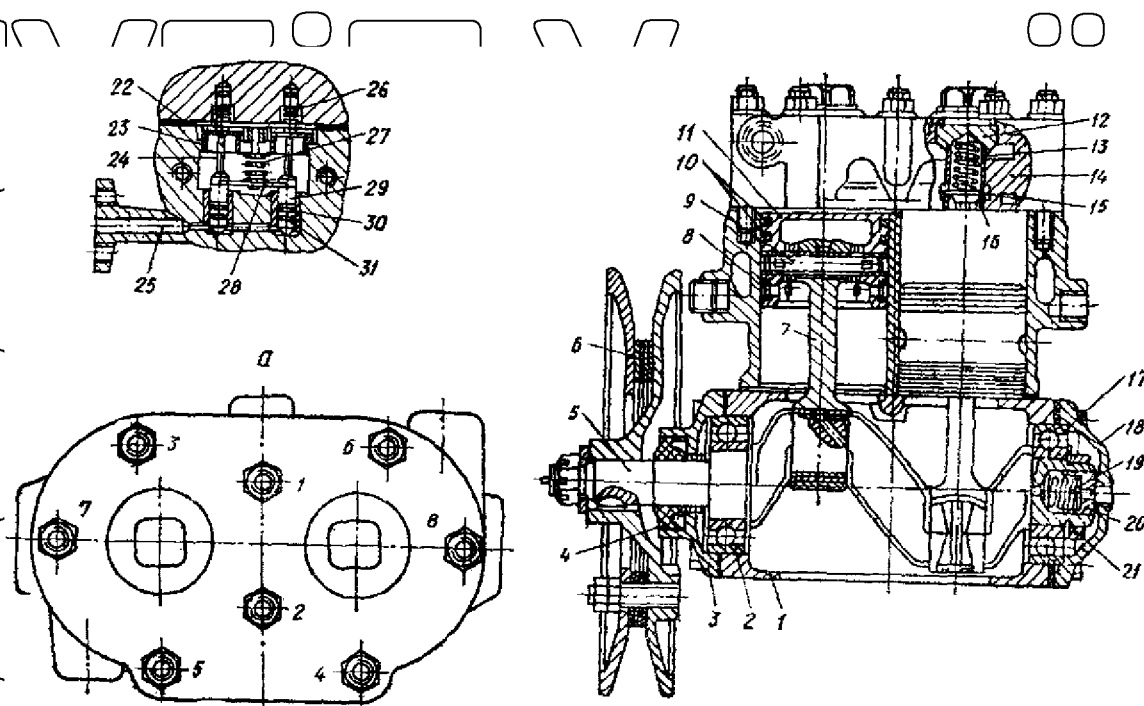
Повітряний компресор. 1 - картер; 2 - передній підшипник колінчатого валу; 3 - стрибка передня; 4 - манжета; 5 - колінчастий вал; 6 - шків; 7 - шатун; 8 - маслоснімне кільце; 9 - поршневий палець; 10 - компресійні кільця; 11 - поршень; 12 - пробка нагнітального клапана; 13 - пружина нагнітального клапана; 14 - головка блоку; 15 - нагнітальний клапан; 16 - сидло нагнітального клапана; 17 - задній підшипник колінчастого валу; 18 - кришка задня; 19 - пружина ущільнювача; 20 - ущільнювач; 21 - гайка кільцева; 22 - впускний клапан; 23 - сидло впускного клапана; 24 - шток впускного клапана; 25 - розвантажувальний канал; 26 - пружина впускного клапана; 27 - пружина коромисла; 28 - коромисло плунжерів; 29 - гніздо шпока впускного клапана; 30 - кільце ущільнювальне; 31 - плунжер впускного клапана; а - схема
